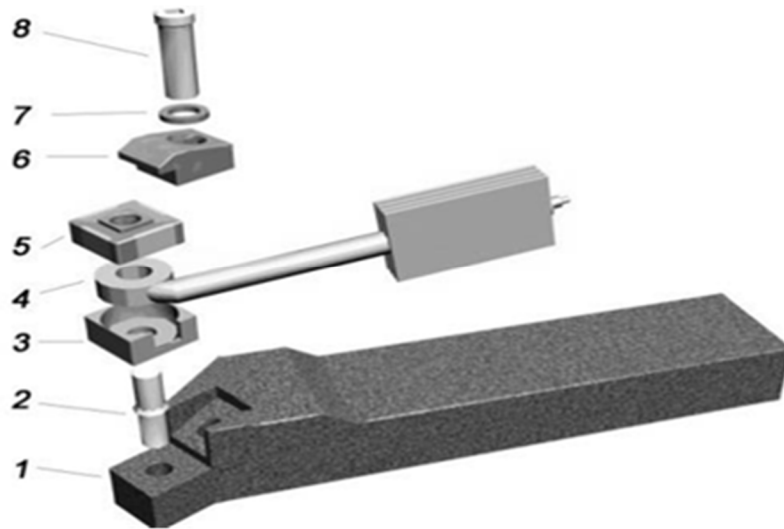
Конструкція різця з кільцевою тепловою трубою (1 – державка; 2 – штифт; 3 – опорна пластина; 4 – теплова труба; 5 – ріжуча пластина; 6 – прижим-стружколом; 7 – шайба; 8 – гвинт)
